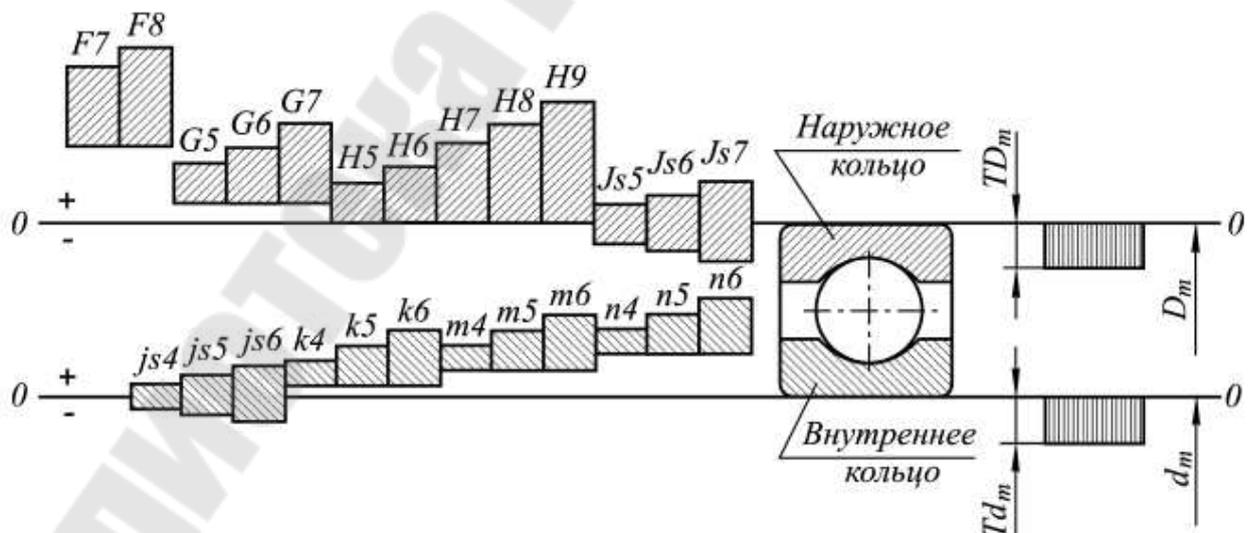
Схемы полей допусков посадок колец подшипников на вал и в корпус при вращении вала с внутренним кольцом подшипника
